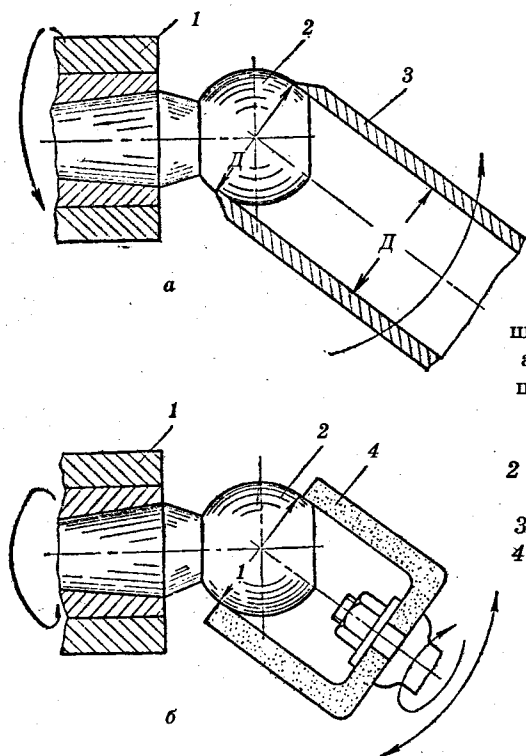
Доводка шаровой поверхности: а — трубчатым резцом, б — шлифовальным кругом,
